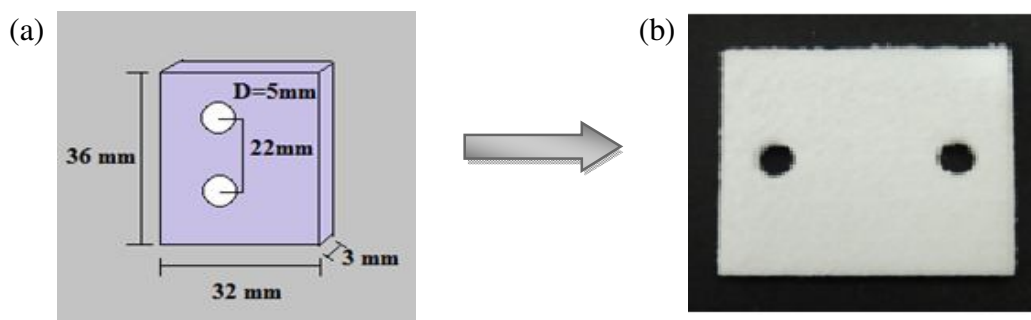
Usinagem das placas porosas (a) Esboço; (b) Placas porosas de PEUAPM obtidas após usinagem.
